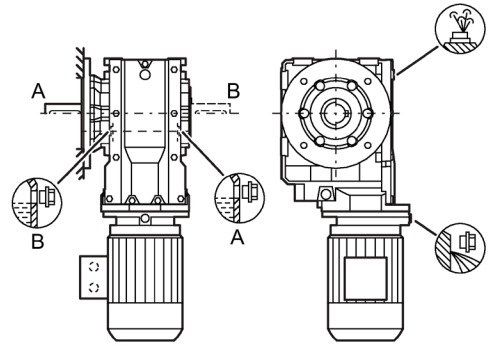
Einbautagen für Kegelradgetriebe B.F Flanschausführung und B.Z mit Gehäuseflansch, Baugröße 19 - 29
